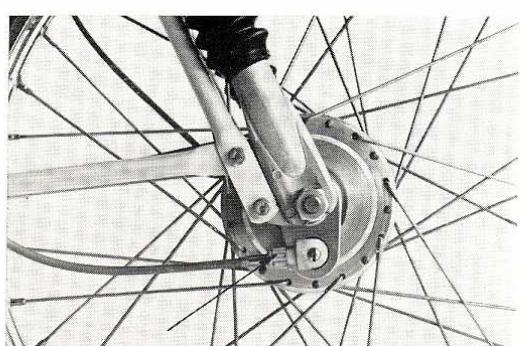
DEMONTAGE DU CABLE DU COMPTEUR KILOMETRIQUE.
